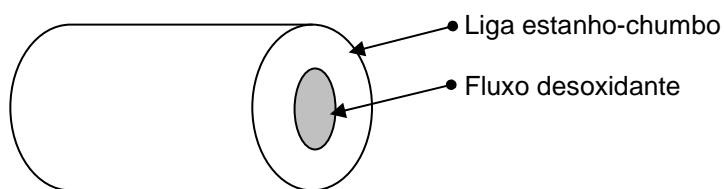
Esquema construtivo de um fio de solda para circuito impresso.
